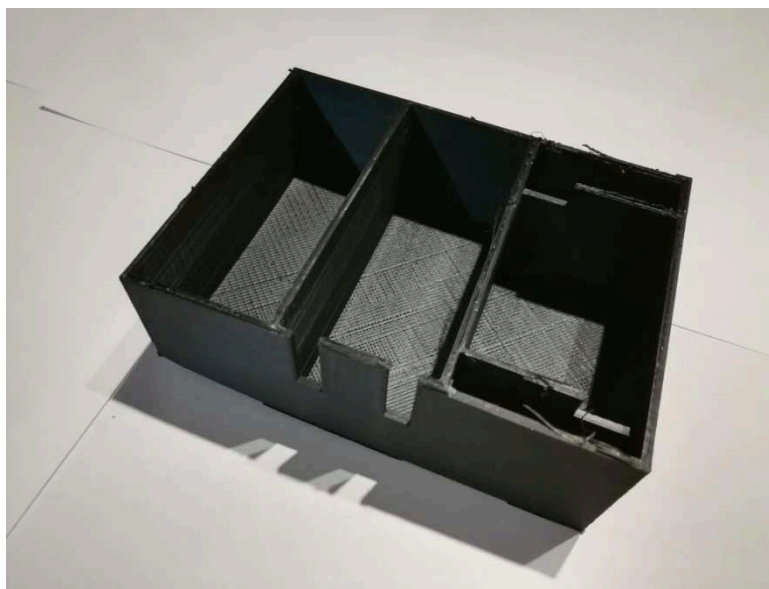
Изготовленный при помощи 3D печати корпус.
